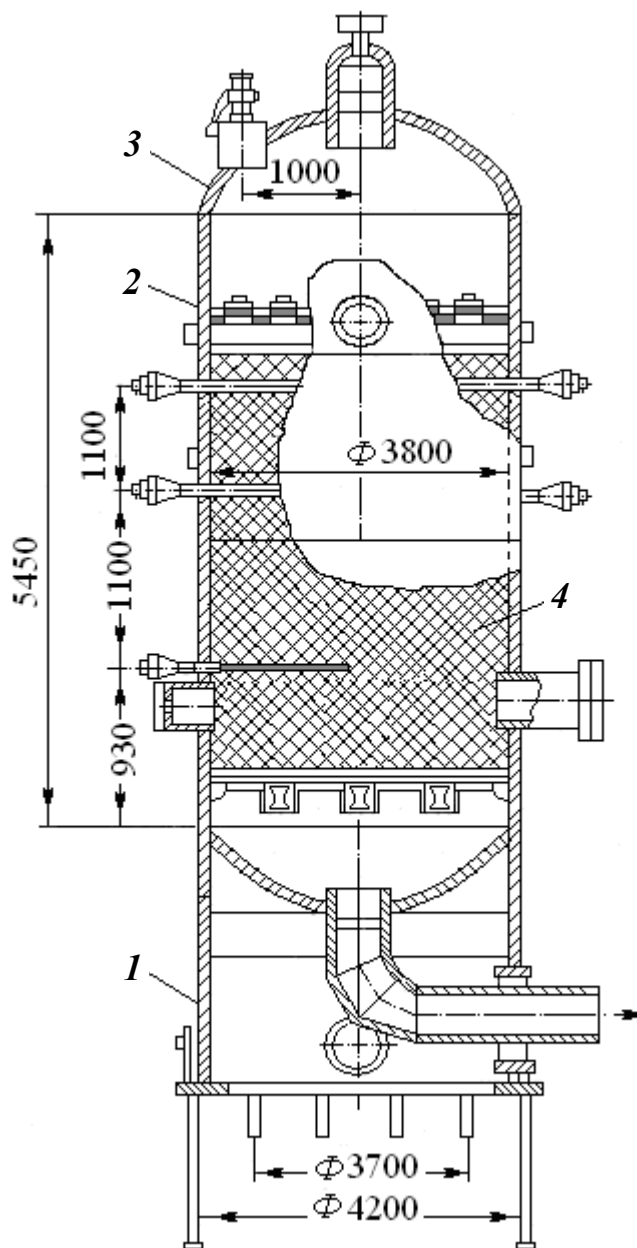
Метанатор: 1 — опора; 2 — обичайка; 3 — кришка; 4 — каталізатор
